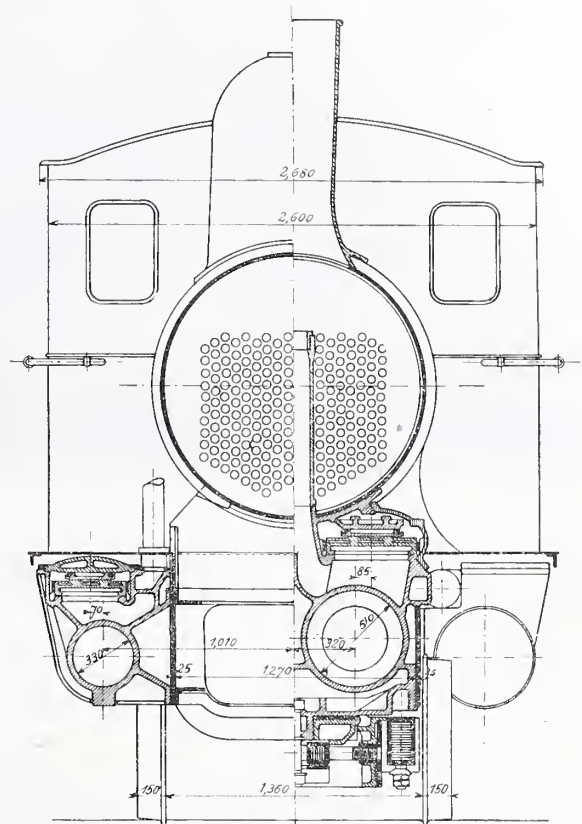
Vierzylinder-Schnellzug-Lokomotive der Schweiz. Centralbahn. — Querschnitt 1 : 40.
